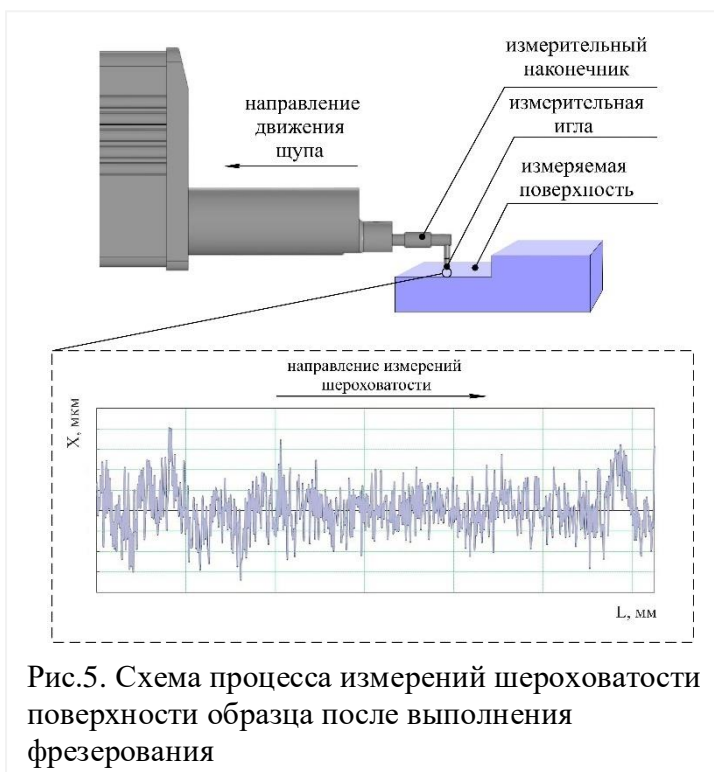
Схема процесса измерений шероховатости поверхности образца после выполнения фрезерования
